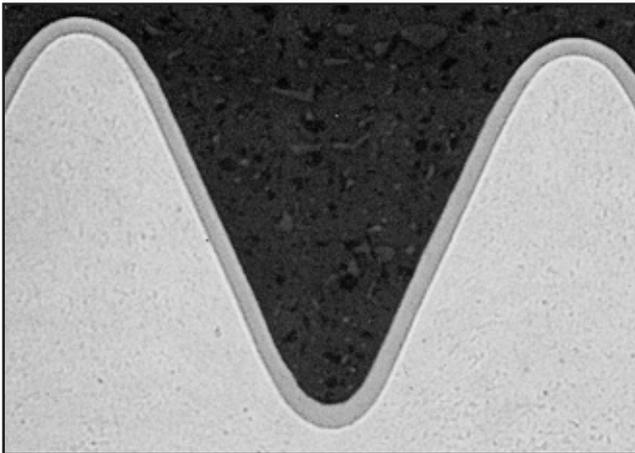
Beschichtetes Gewinde Figure 3 Coated thread
